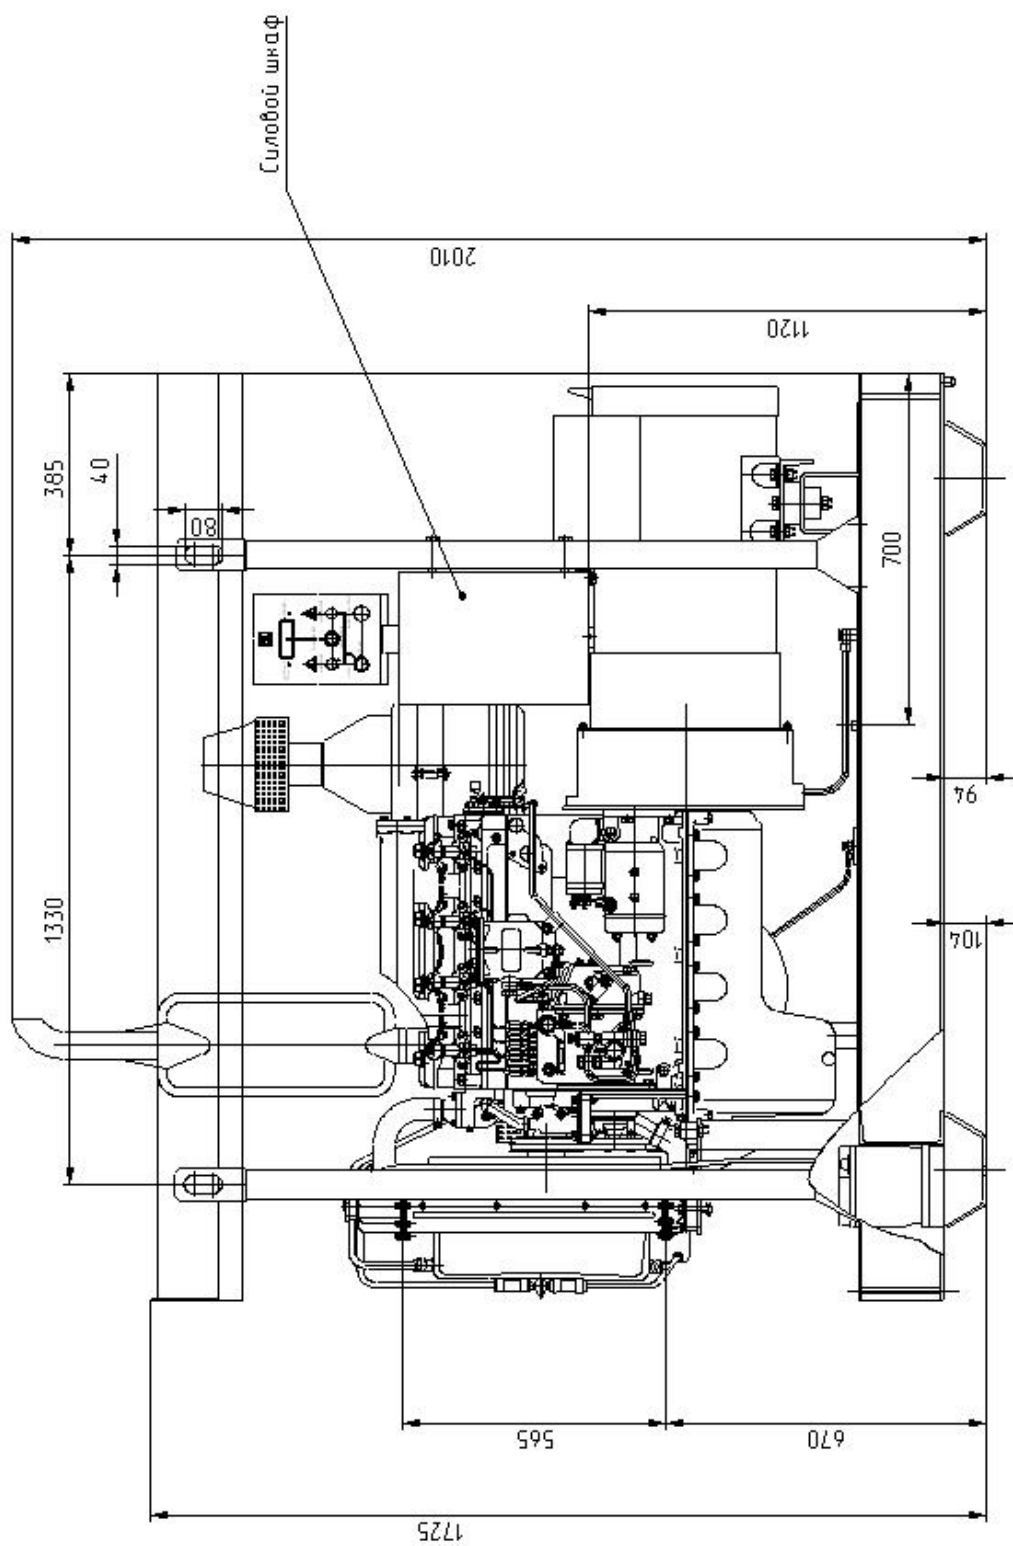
Монтажный чертеж установки ДГ-40 (вид сбоку).
